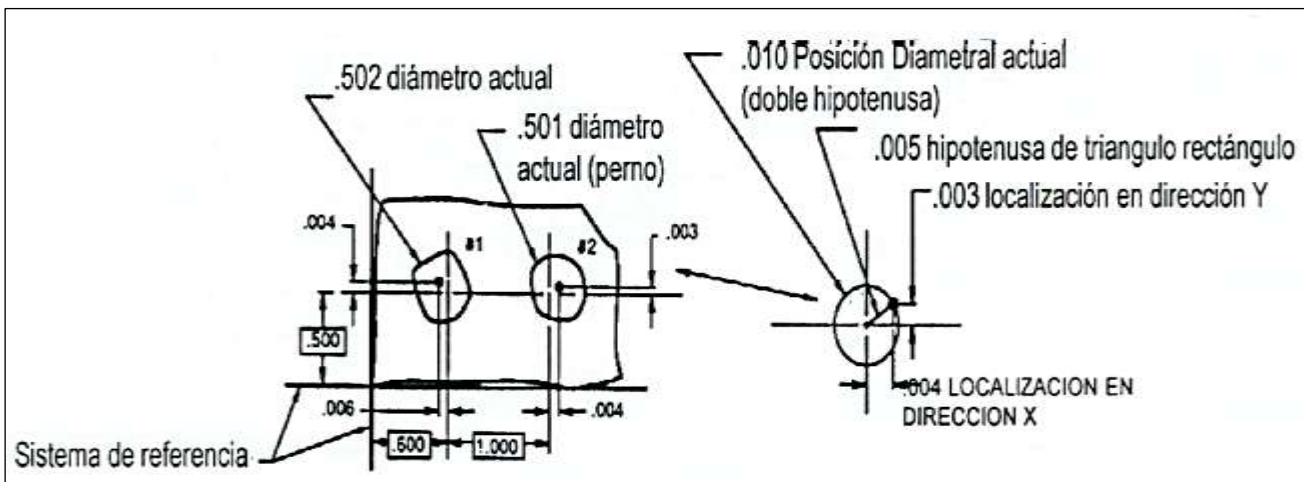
Ejemplo Tolerancia de Posición
